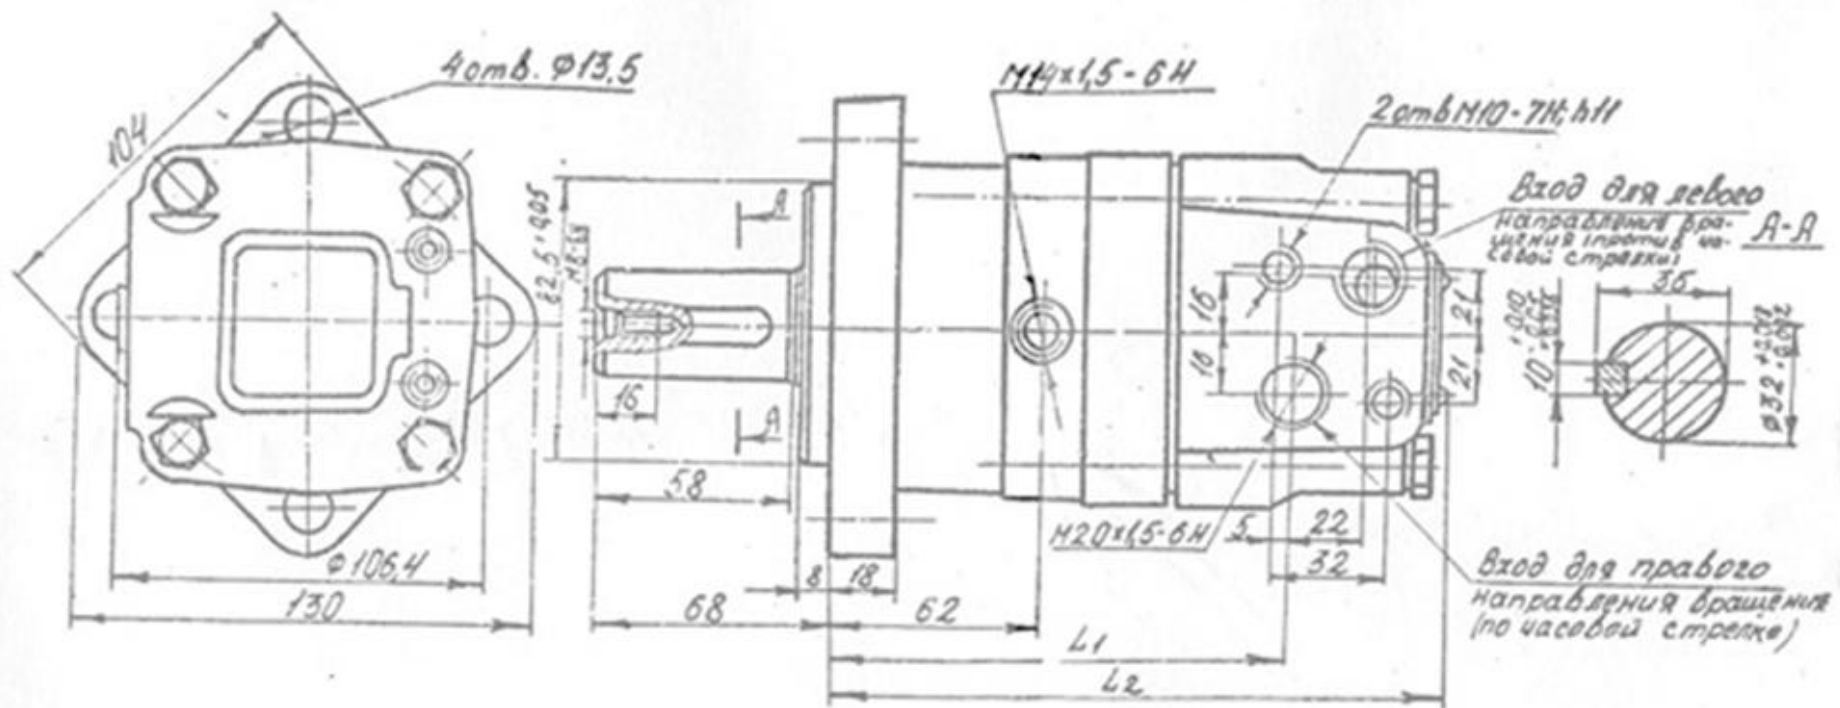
Габаритно-присоединительные размеры гидромоторов серии типа МГП-80, МГП -100, МГП -125 и МГП -160 (могут согласовываться с заказчиком)
